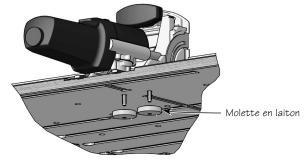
Montage de la fraiseuse au plateau (base retirée aux fins de présentation)
